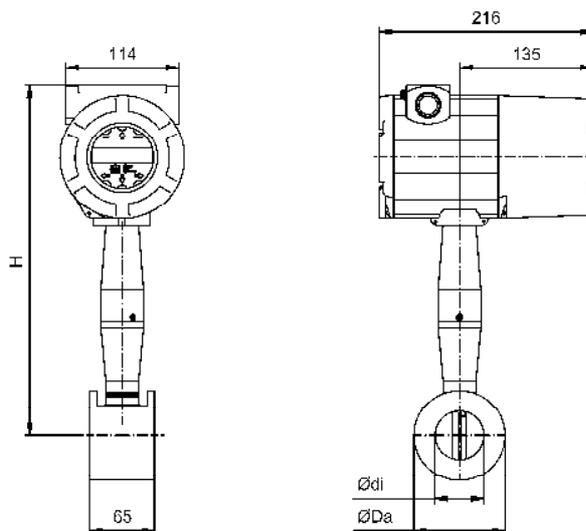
Dimensionen Zwischenflansch mit aufgebauter Elektronik
